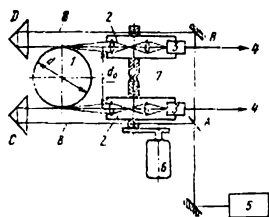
Лазерна система контролю діаметра деталі на токарному верстаті
